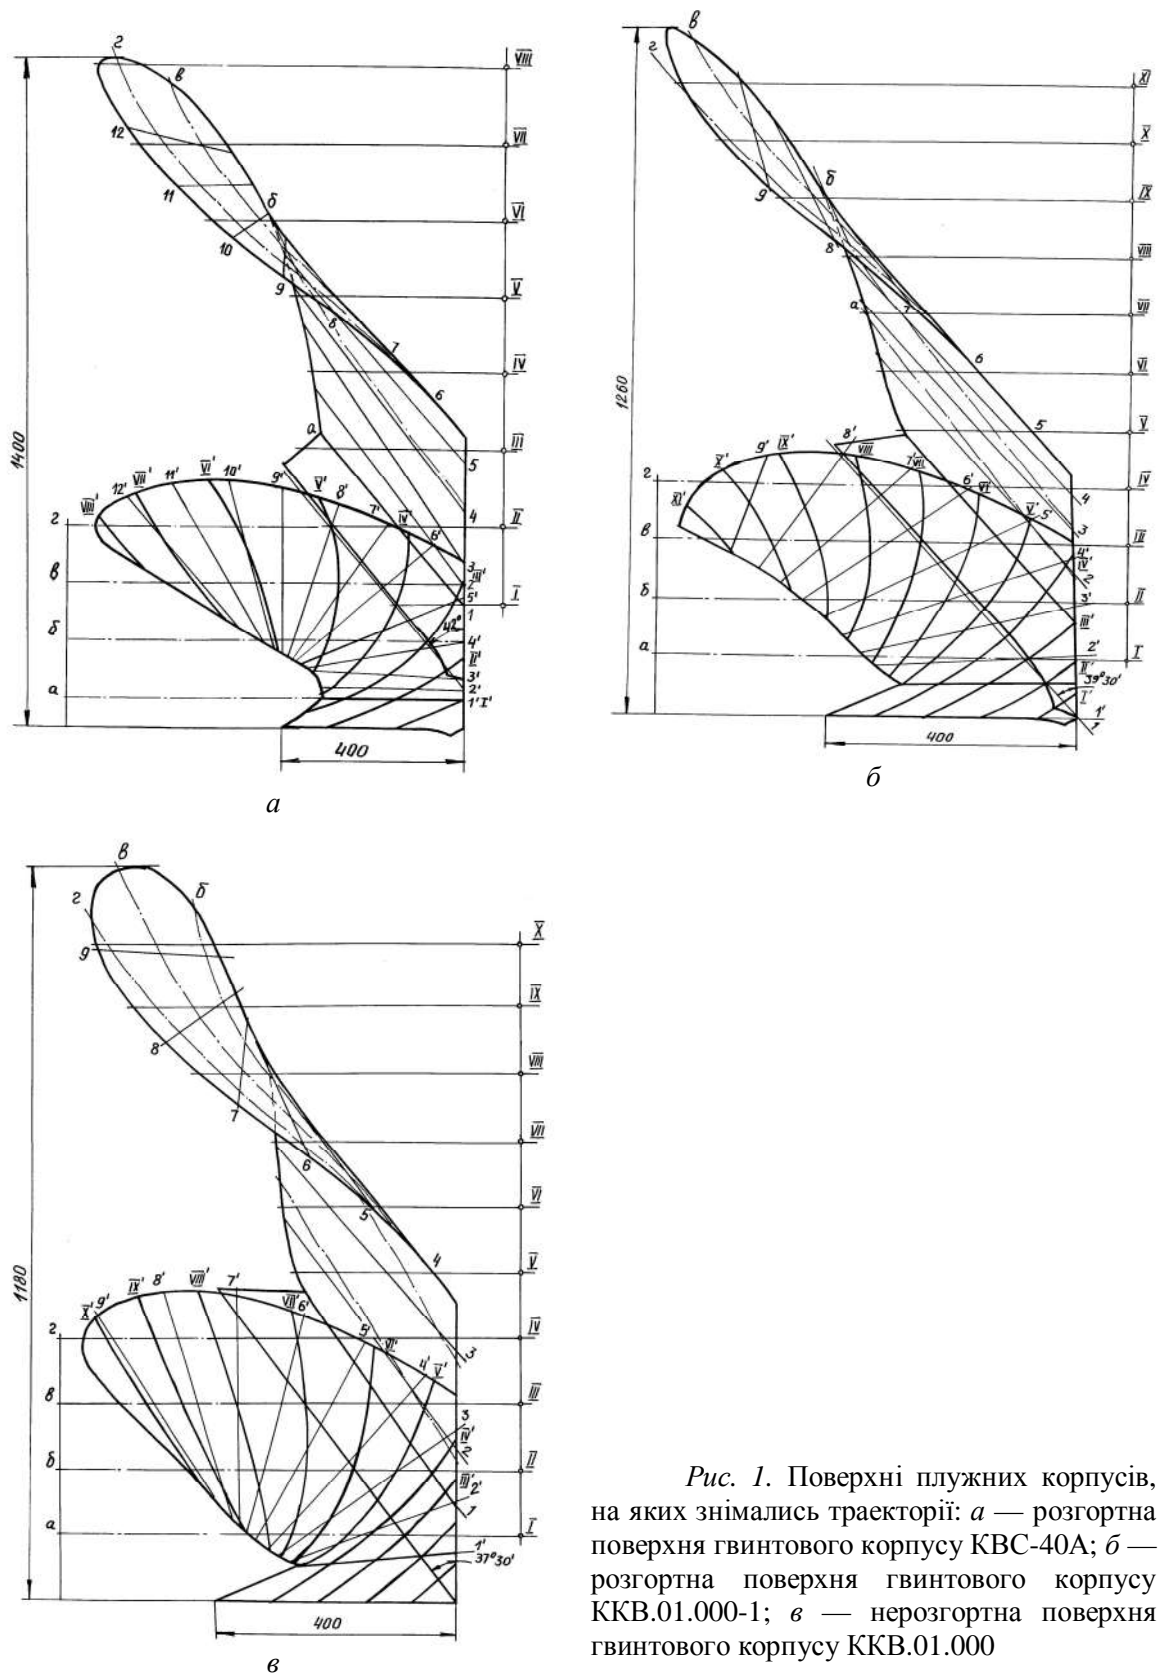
Поверхні плужних корпусів, на яких знімалися траєкторії: *a* — розгортна поверхня гвинтового корпусу КВС-40А; *б* — розгортна поверхня гвинтового корпусу ККВ.01.000-1; *в* — нерозгортна поверхня гвинтового корпусу ККВ.01.000
